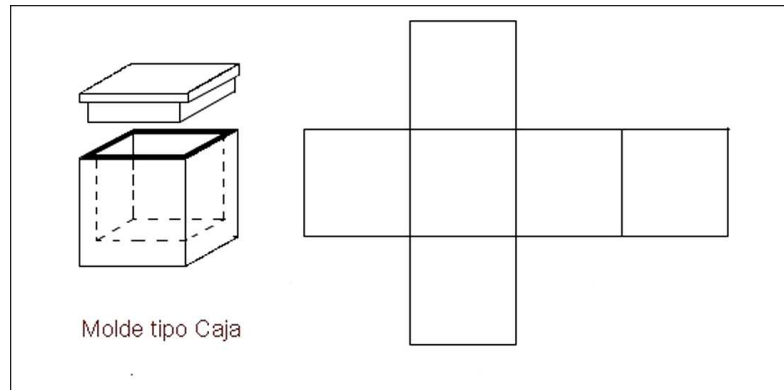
Molde metálico típico, tipo caja, para moldeo por compresión. [ADVANI]
